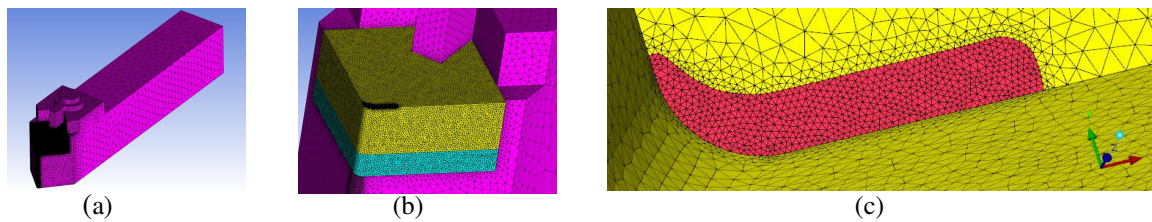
Malha tetraédrica típica utilizada: (a) Vista geral (b) Vista, em detalhe, da ferramenta de corte (c) Detalhe da região da interface “cavaco-ferramenta”
